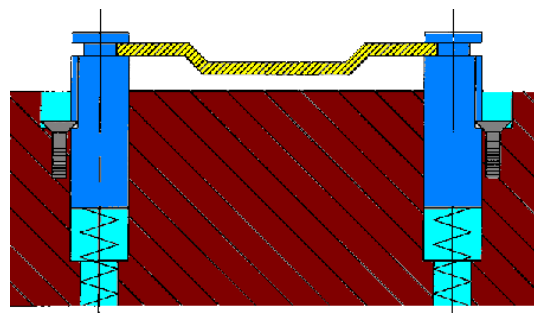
Přítlačování materiálu odpruženým ramen [58]
